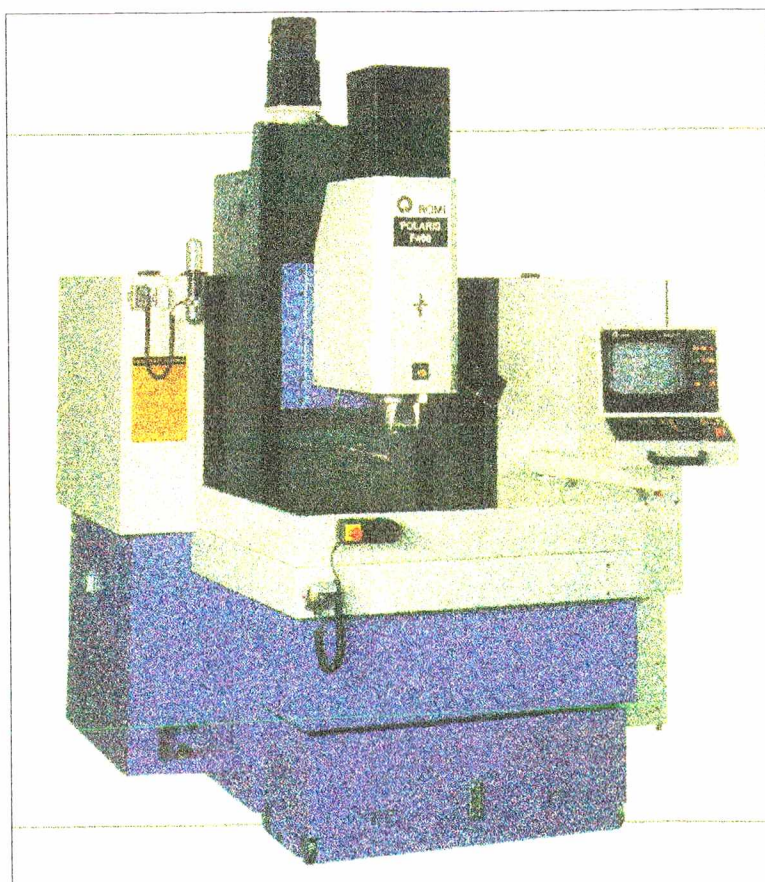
Máquina-ferramenta Romi F400 [38].
